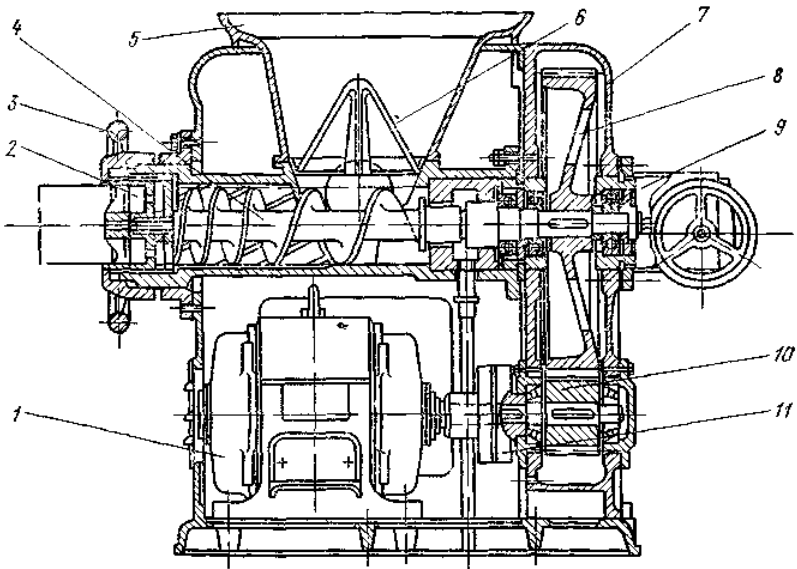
Вовчок МП-2-220: 1 – електродвигун; 2 – комплект ріжучого механізму; 3 – гайка-маховик, 4 – робочий шнек; 5 – завантажувальна чаша; 6 – запобіжник; 7 – корпус редуктора; 8 – зубчасте колесо; 9 – механізм виштовхування робочого шнека; 10 – шестірня; 11 – пружна втулково-пальцева муфта
